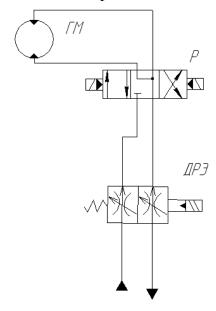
Гидропривод поворотного механизма инструментального магазина барабанного типа
